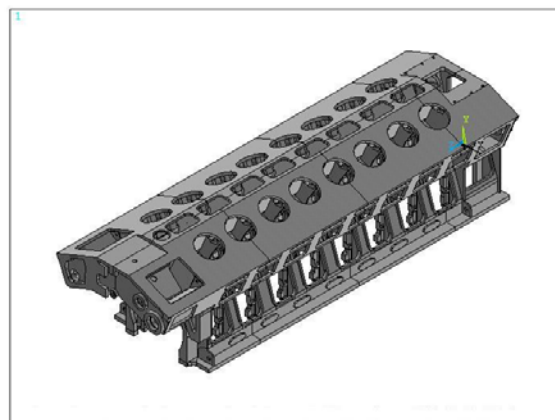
Общий вид проекта корпуса дизеля 1Д80Б 02 004
